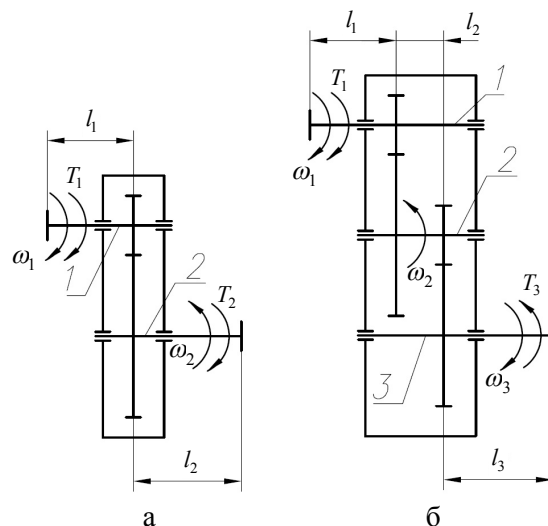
Кинематические схемы зубчатых редукторов: а – одноступенчатого; б – двухступенчатого
